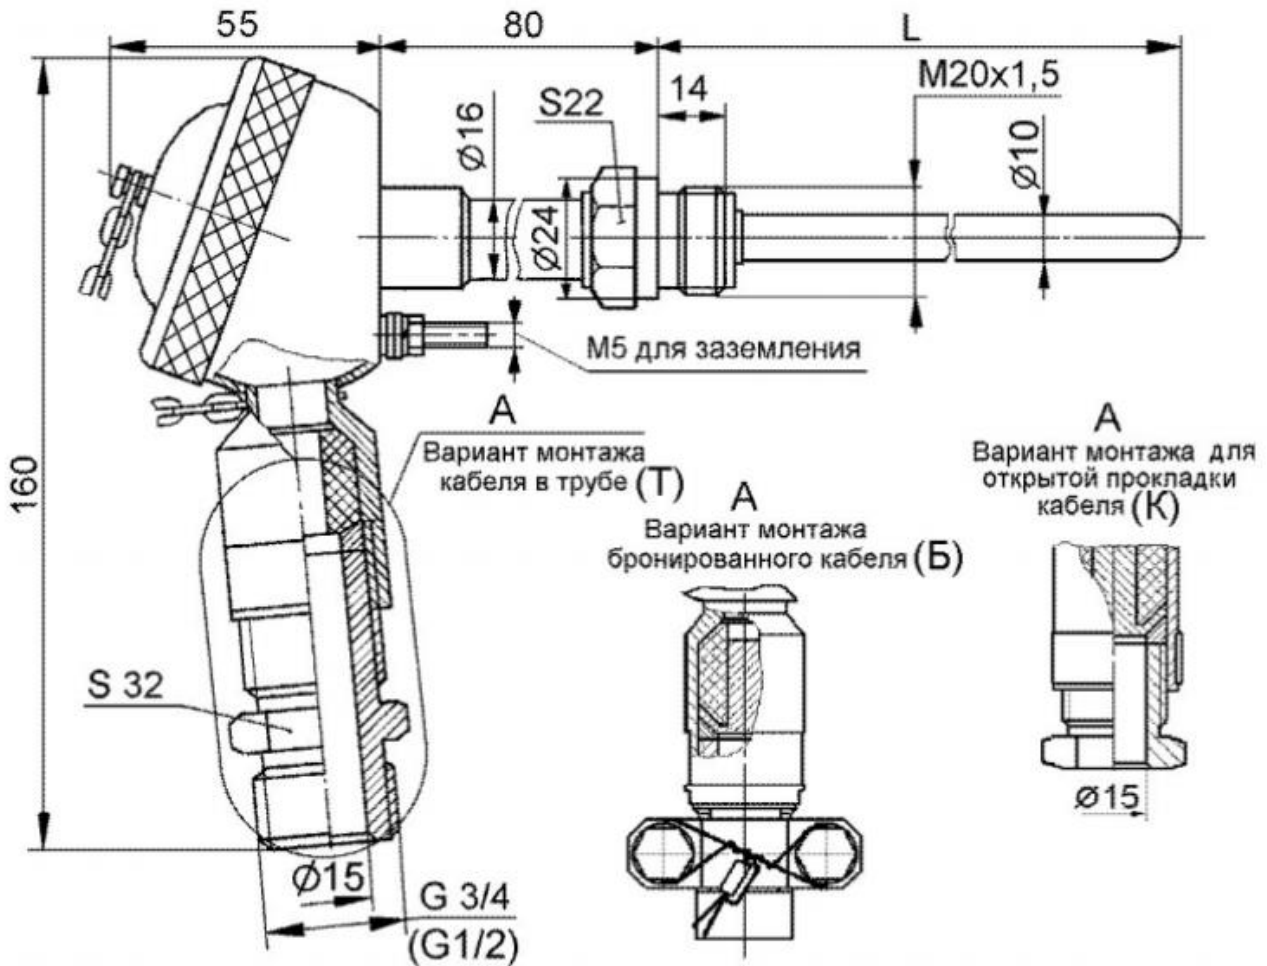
Головка из нержавеющей стали, штуцер неподвижный
